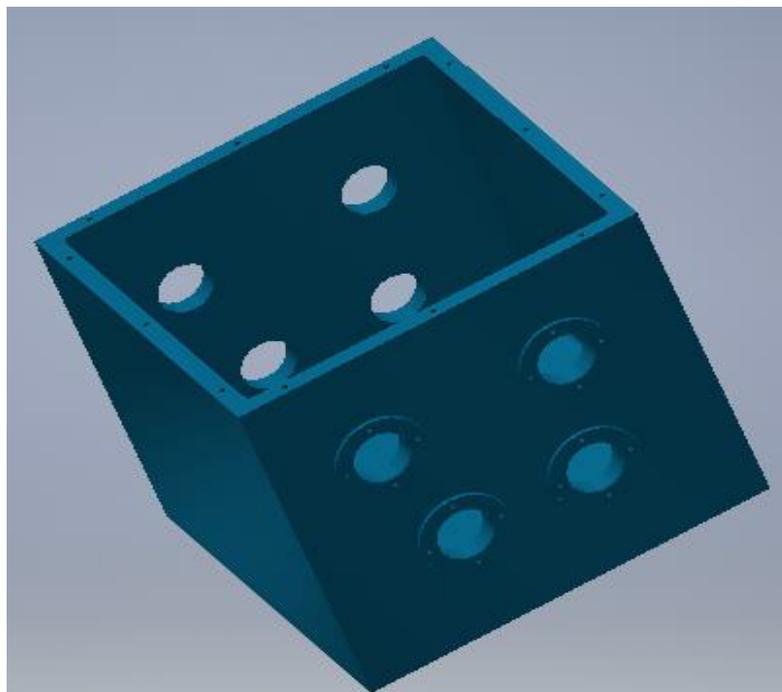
Трехмерная модель коробки передач токарного станка
